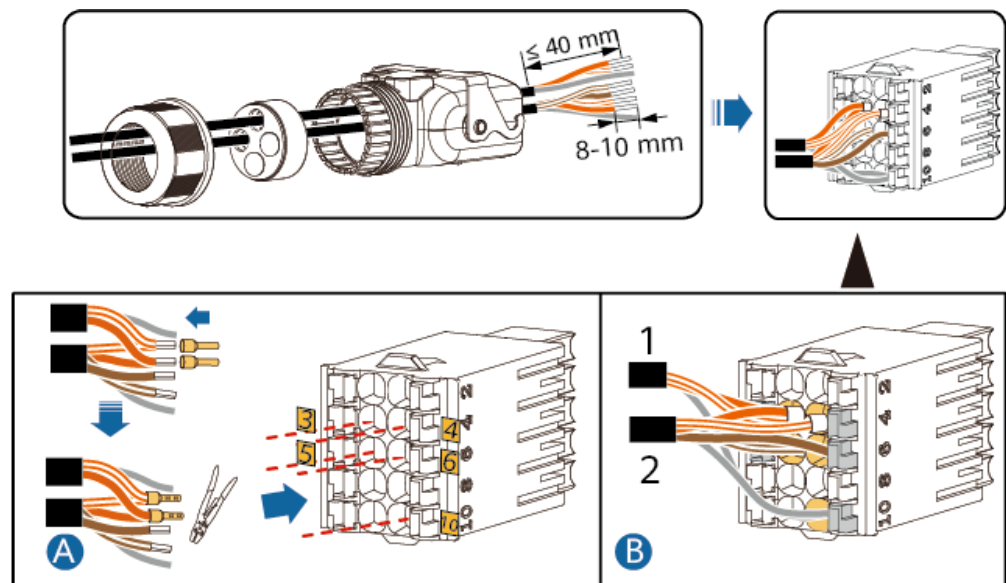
Installazione del cavo (collegamento al contatore elettrico)
